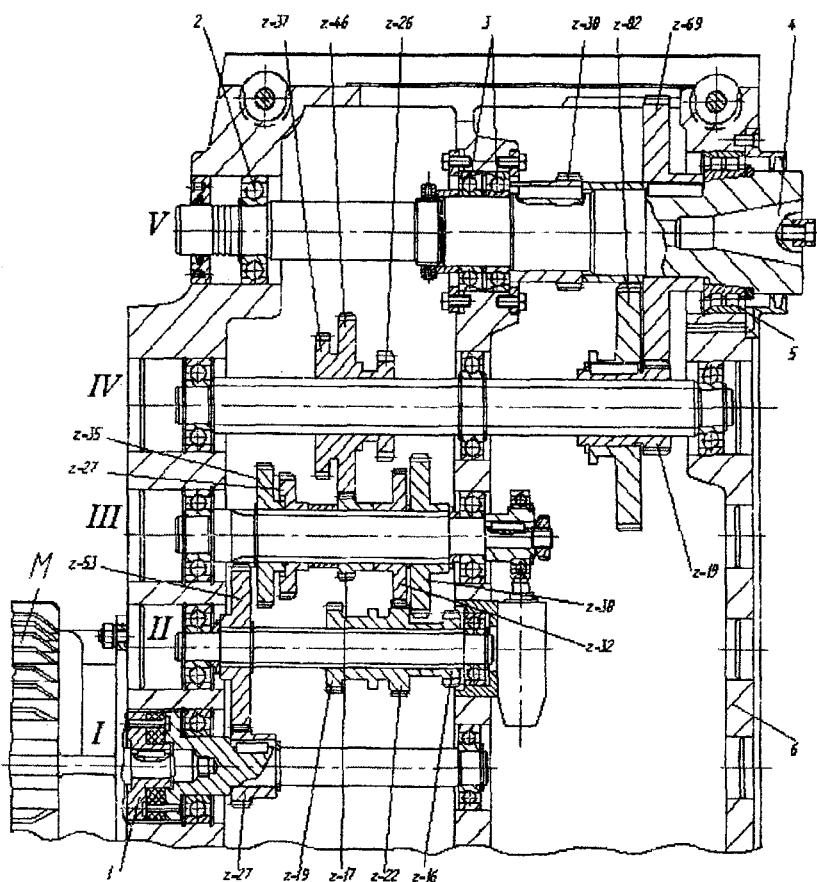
Главный привод горизонтального консольно-фрезерного станка модели 6М82
